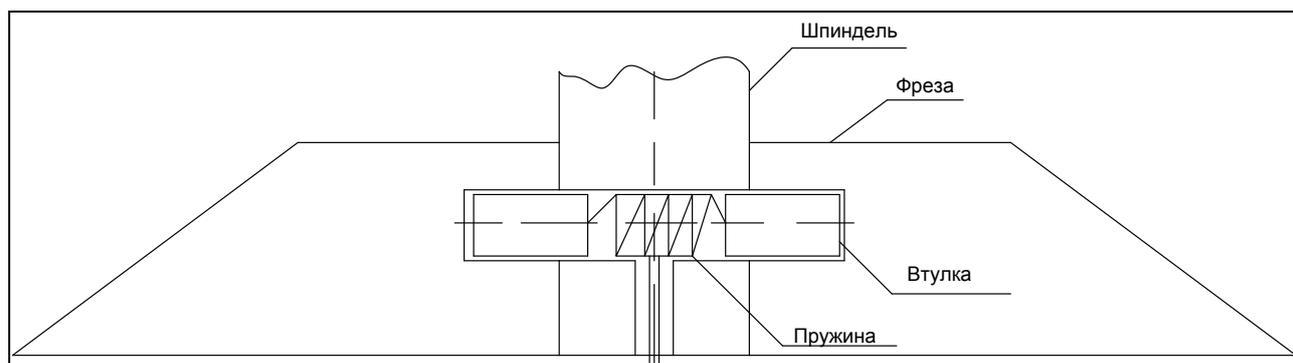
Безболтовое крепление фрезы к шпинделю
